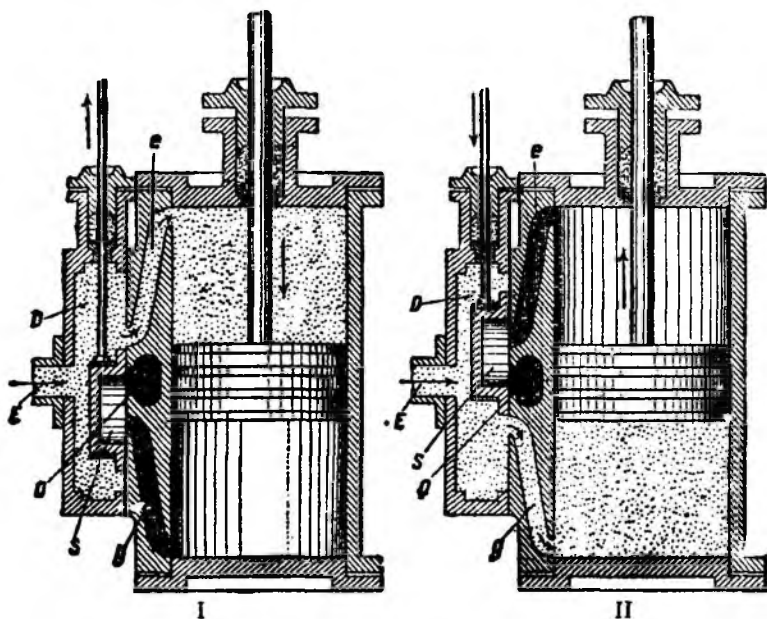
Паровой цилиндр с поршнем и золотниковой коробкой:
